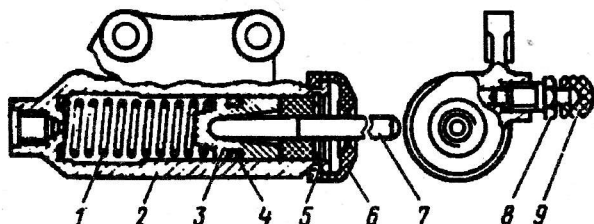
Рабочий цилиндр привода выключения сцепления:
